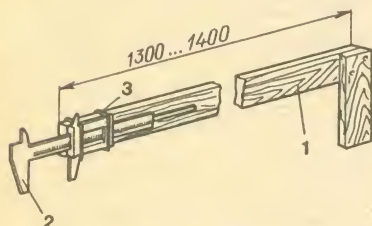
Приспособление для замера схождения из рейки и штангенциркуля: 1 — рейка; 2 — штангенциркуль; 3 — скоба или струбцина.
